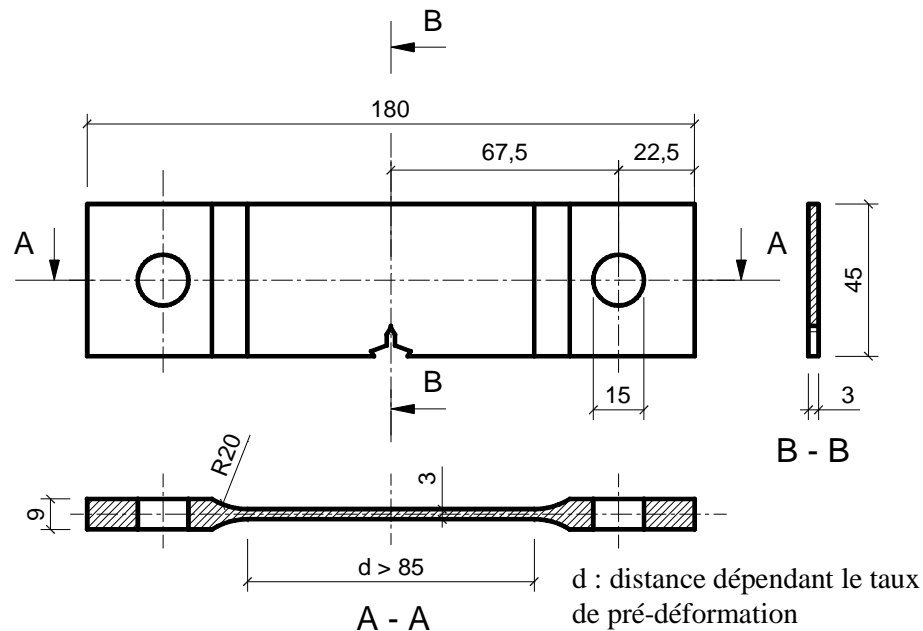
Eprouvette SENT pré-déformée obtenue par re-usinage de l'ébauche
